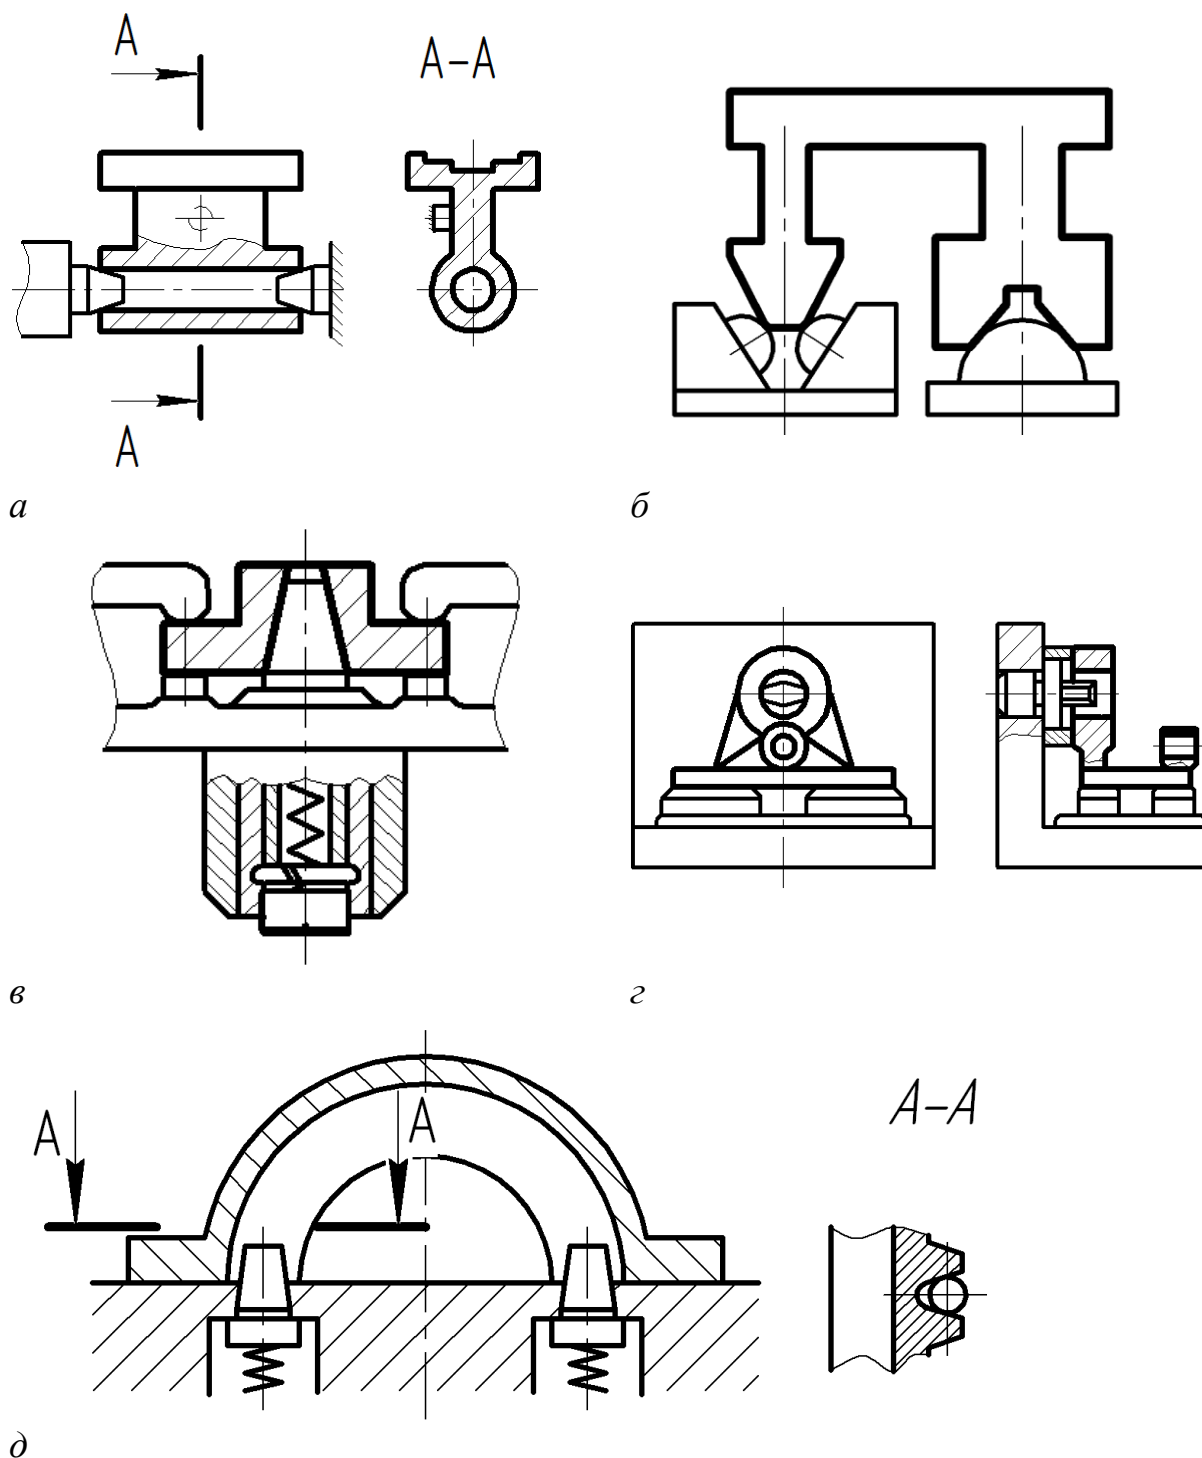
Комбинированные схемы установки корпусных деталей:
